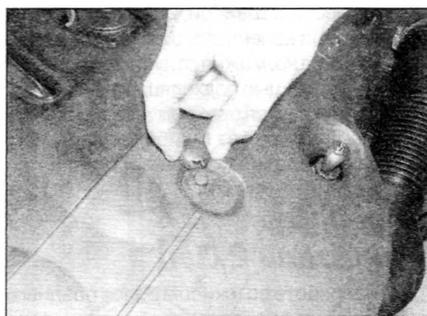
, б. ...и на верхней плоскости крышки двигателя...
